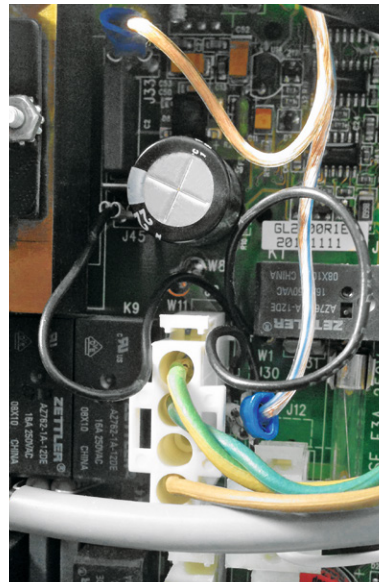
Die Steckbrücke für die Whirlpool-Beleuchtung
